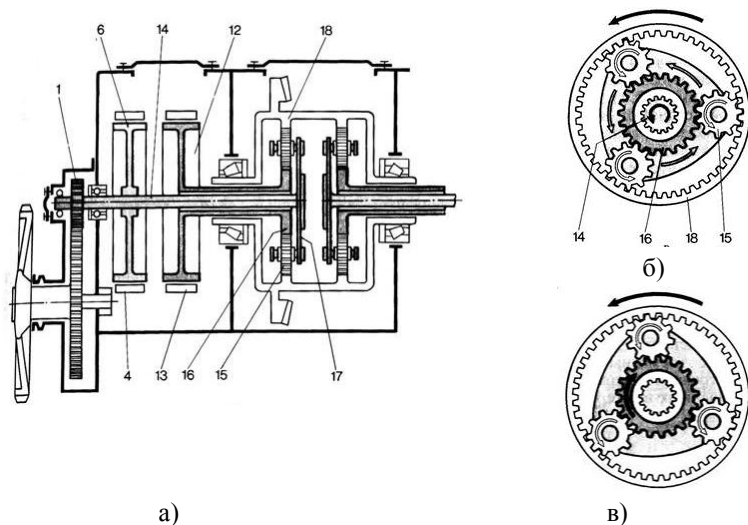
Схема планетарного механизма поворота: а - схема; б - взаимодействие шестерен при прямолинейном движении трактора; в - взаимодействие шестерен при повороте; 1 - ведущая шестерня конечной передачи; 4 - тормозная лента остановочного тормоза; 6 - шкив остановочного тормоза; 12 - шкив тормоза солнечной шестерни; 13 - тормозная лента солнечной шестерни; 14 - полуось (вал); 15 - сателлит; 16 - солнечная шестерня; 17 - водило; 18 - коронная шестерня
